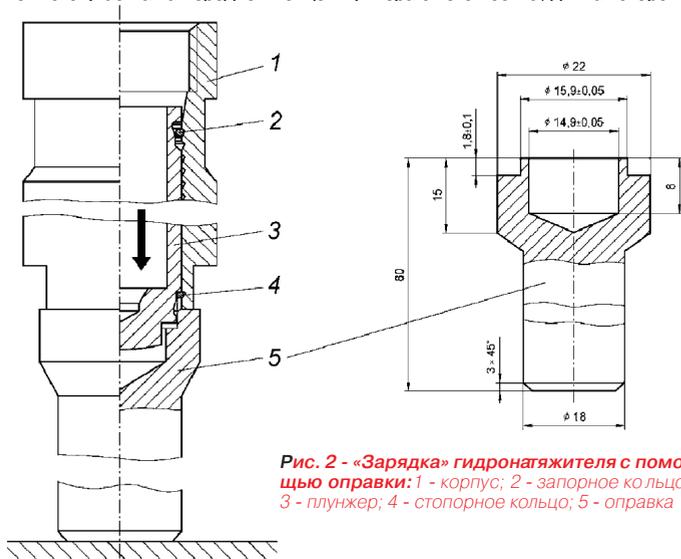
«Зарядка» гидронатяжителя с помощью оправки: 1 - корпус; 2 - запорное кольцо; 3 - плунжер; 4 - стопорное кольцо; 5 - оправка
